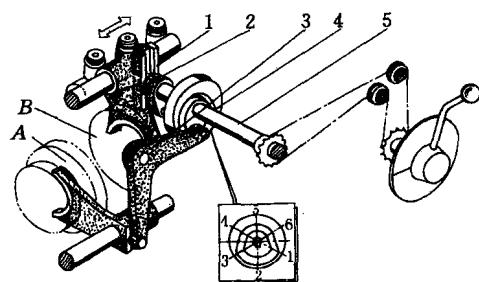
轴Ⅱ及轴Ⅲ上滑动齿轮的操纵机构
